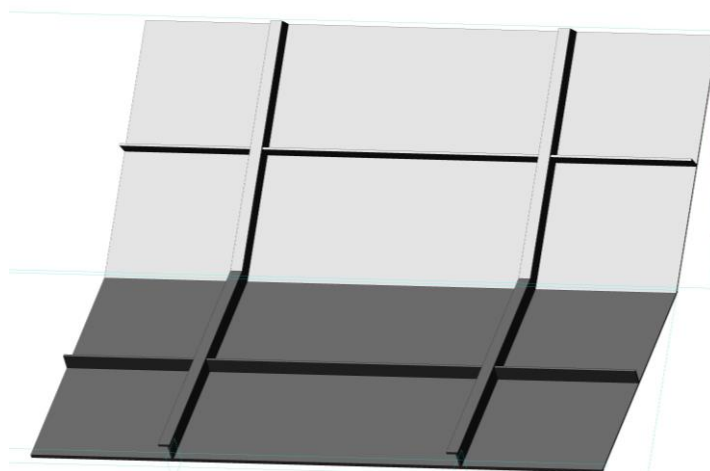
Модель части корпуса для расчета на сварочные деформации и напряжения
